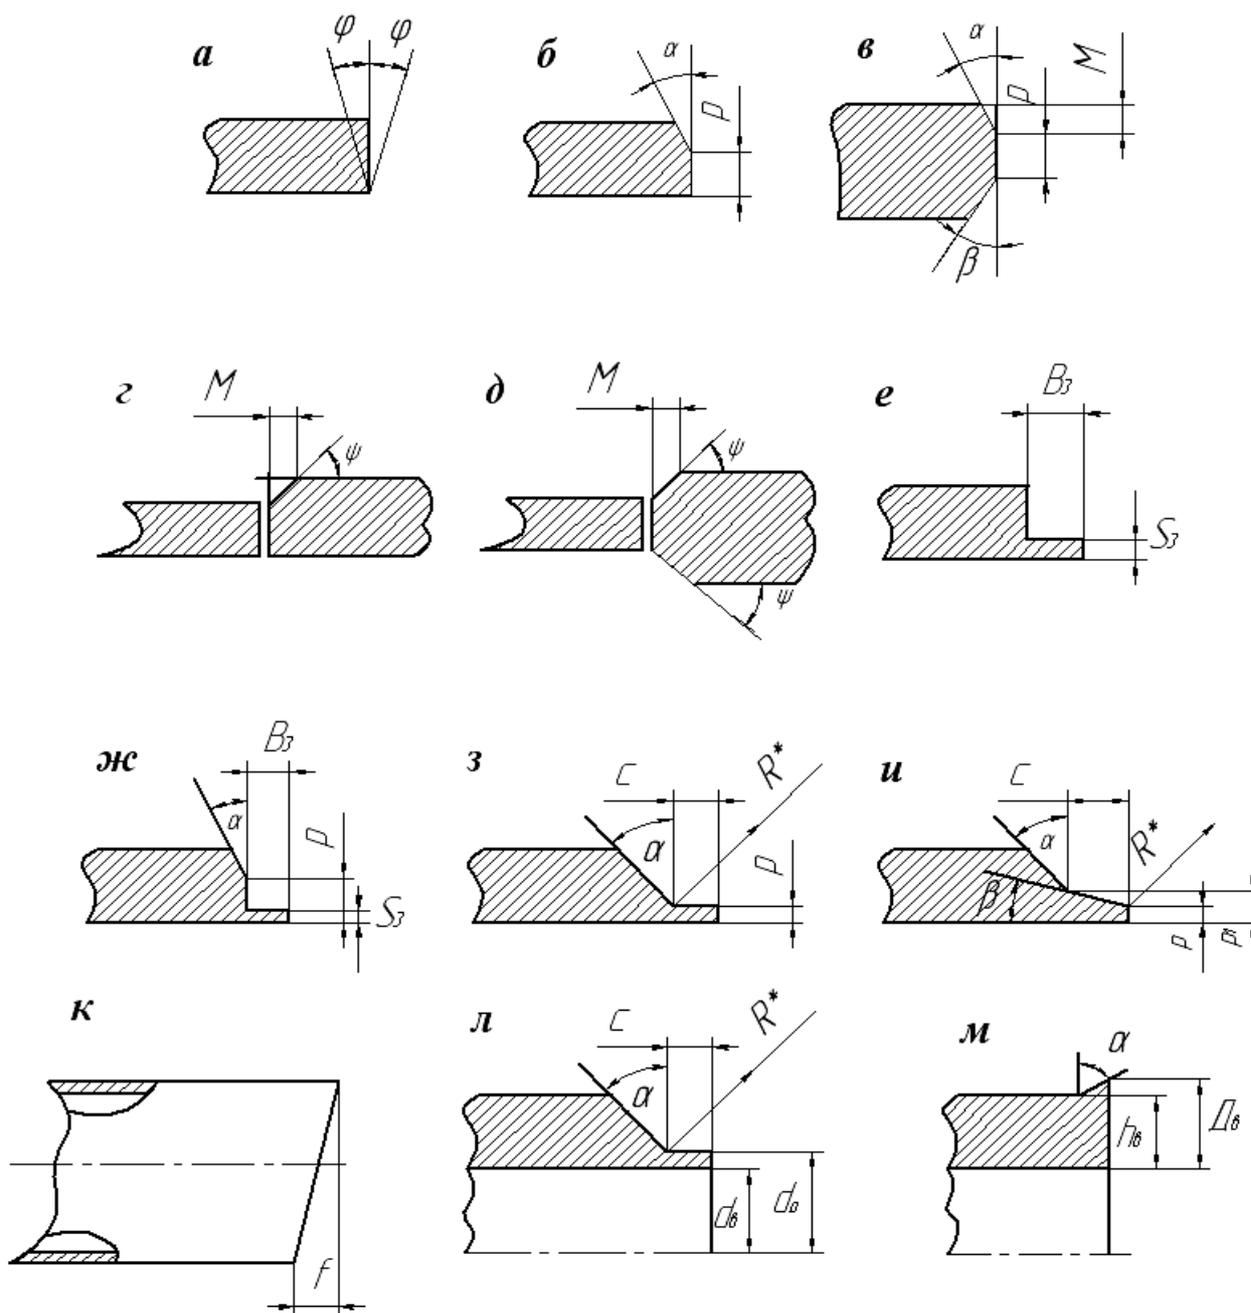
Размеры, контролируемые измерением при подготовке деталей под сварку (начало): *a* – I-образная разделка кромки (без скоса кромки); *б* – V-образная односторонняя разделка кромки; *в* – V-образная двухсторонняя разделка кромки; *г*, *д* – подготовка к сварке стыкового соединения деталей, значительно отличающихся по толщине; *е*, *ж* – подготовка к сварке замкового соединения; *з* – U-образная разделка кромки; *и* – V-образная двухсторонняя разделка кромки; *к* – отклонение от перпендикулярности торца трубы; *л* – подготовка кромок штуцера D_y 10–65; *м* – I-образная разделка с присадочным выступом. *Примечание.* Размер измерению не подлежит, так как обеспечивается режущим инструментом и оценивается визуально
